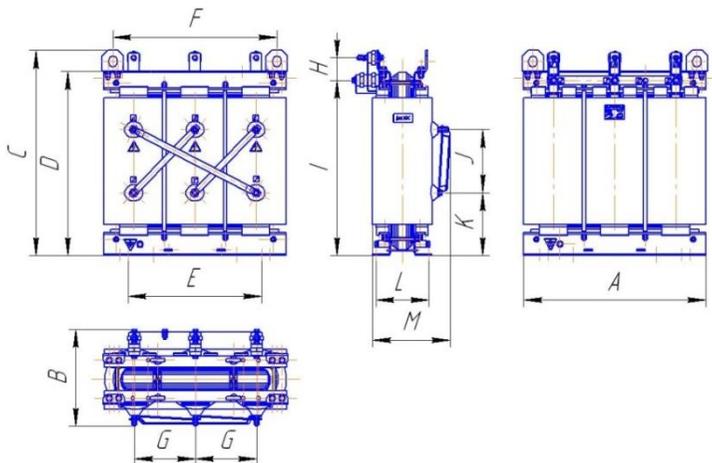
а – Габаритные, установочные и присоединительные размеры трансформатора
